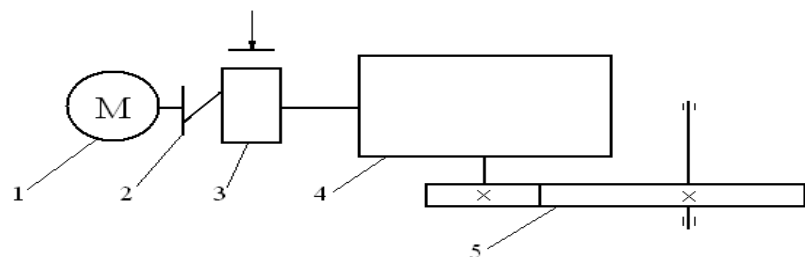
Кинематическая схема привода механизма поворота крана на неподвижной опоре: 1 – электродвигатель 4АС90ЛА8У3; 2 – муфта МУВП; 3 – тормоз ТКТ-100; 4 – редуктор 4-125; 5 – открытая зубчатая передача
